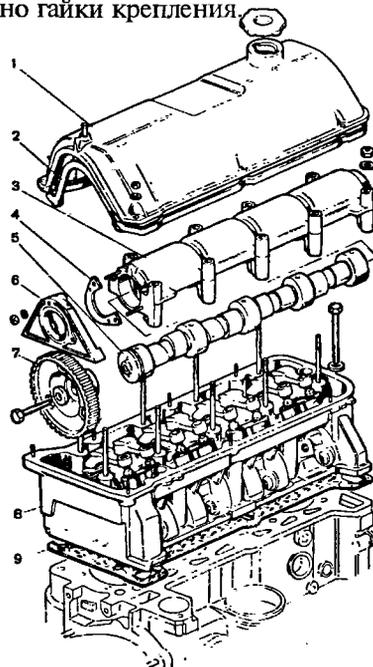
Снятие головки цилиндров: 1 - крышка головки цилиндров; 2 - прокладка; 3 - корпус подшипников распределительного вала; 4 - упорный фланец; 5 - распределительный вал; 6 - держатель сальника распределительного вала; 7 - шкив распределительного вала; 8 - головка цилиндров; 9 - прокладка головки цилиндров
